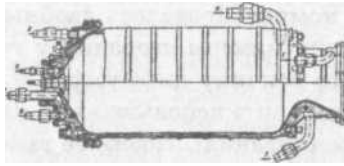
Жидкостный ракетный двигатель Д-1-А-1100
